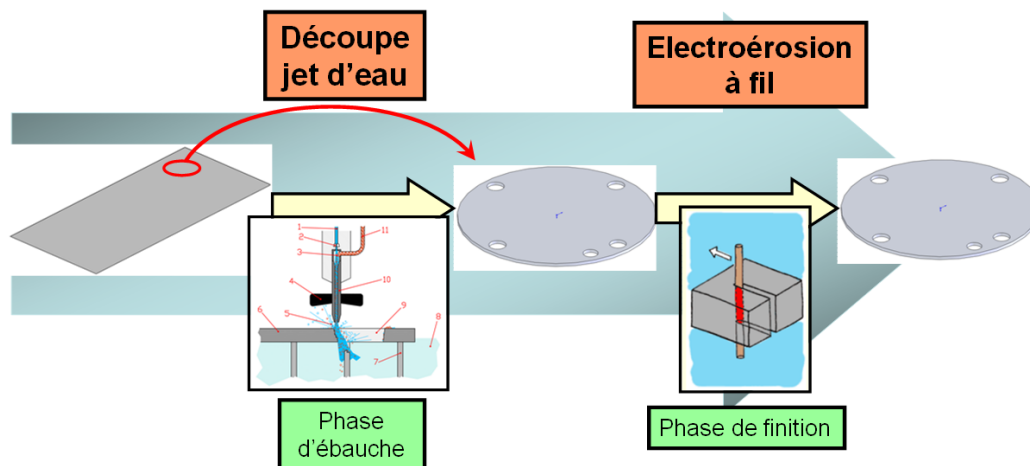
Processus de fabrication des éprouvettes de soudage
